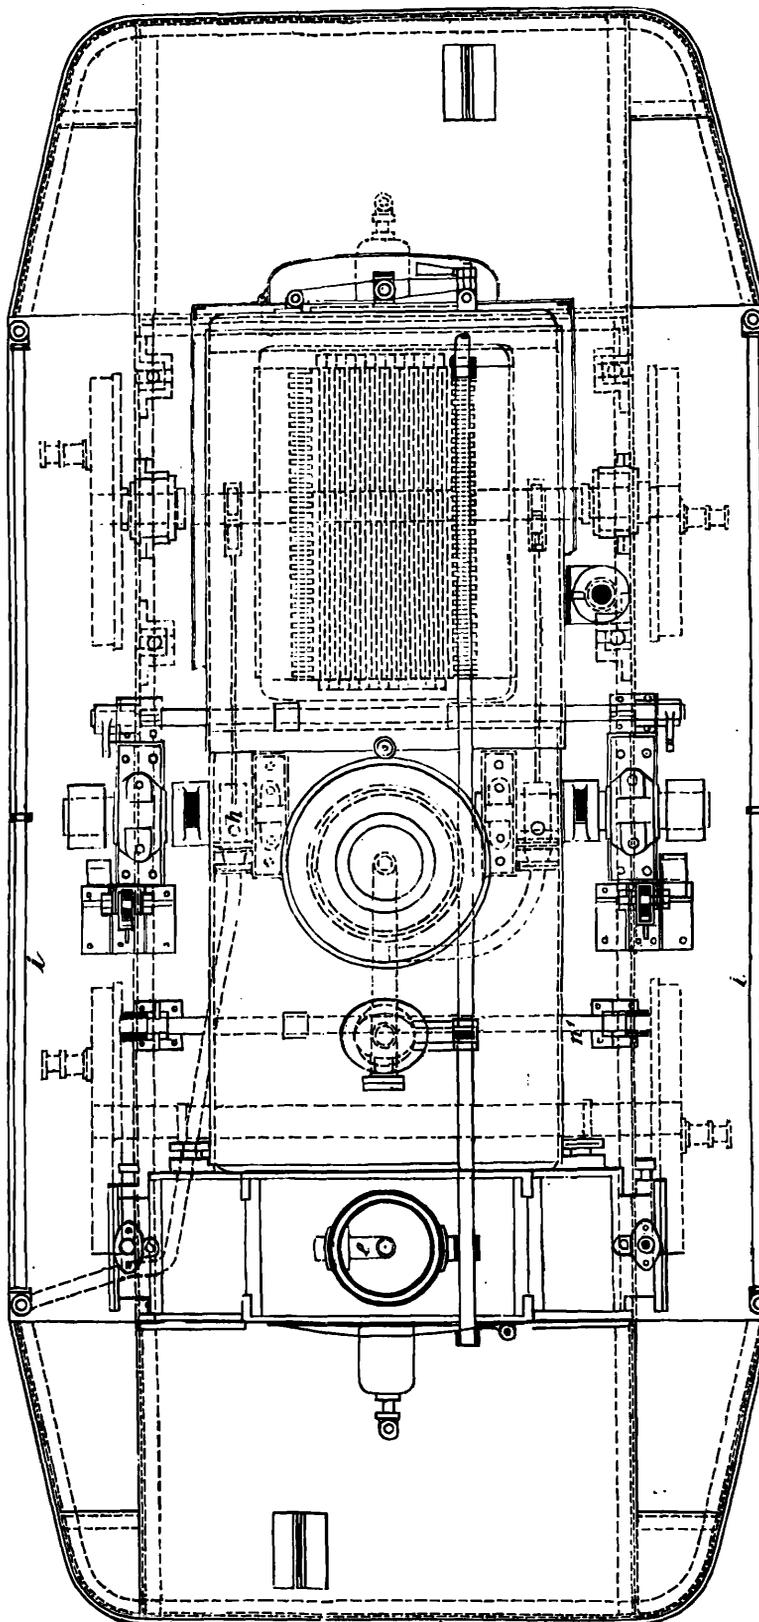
Grundriss der Strassenbahnlocomotive, System Schwartzkopf.
